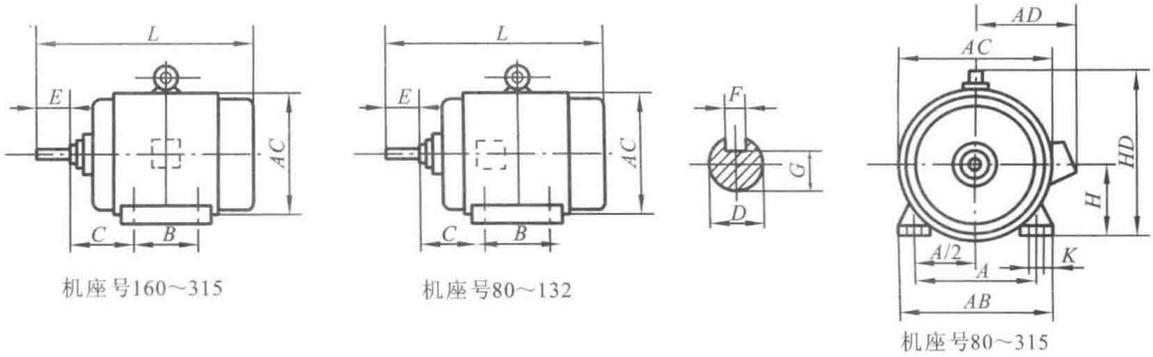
Y160M-4 型电动机的外形及安装尺寸
